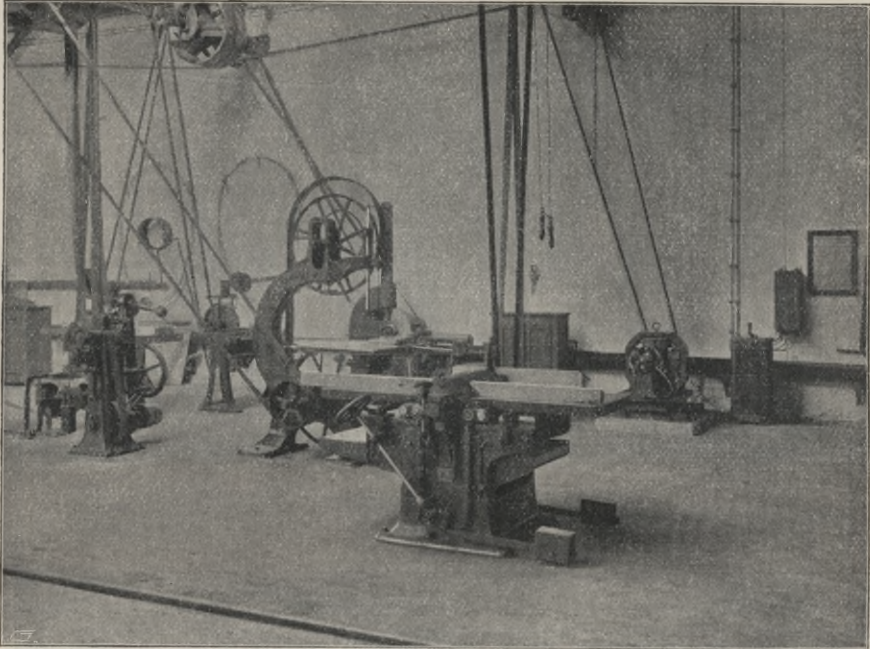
Gruppenantrieb von Holzbearbeitungsmaschinen in einer Tischlerei.
